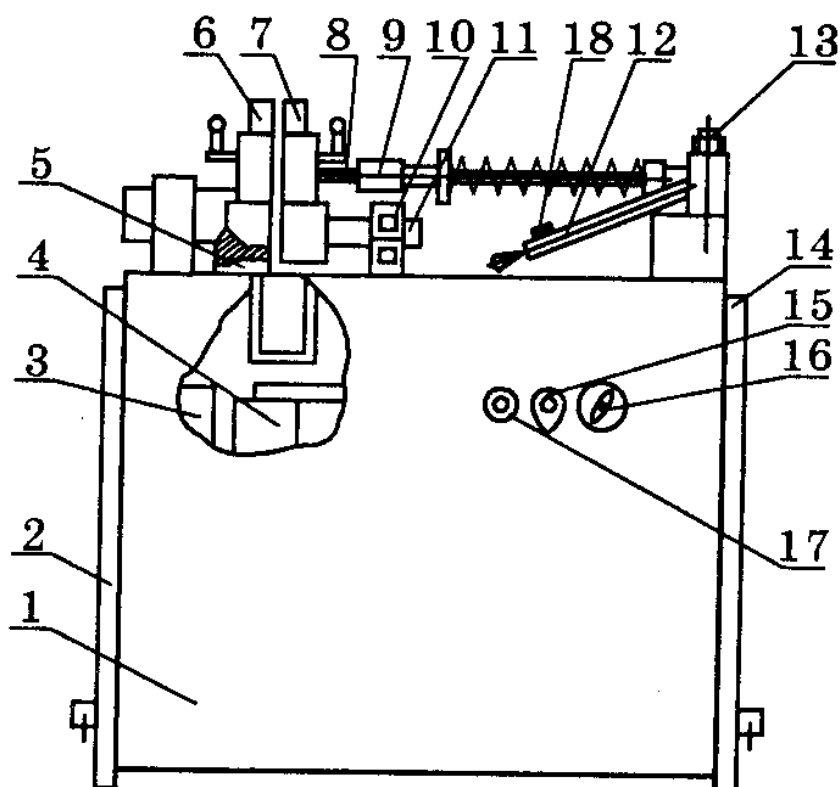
Машина для стыковой сварки МС-802
